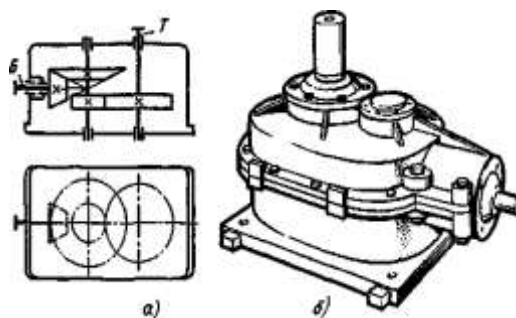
Двухступенчатый коническо-цилиндрический редуктор с вертикальным тихоходным валом: *а* – кинематическая схема; *б* – общий вид
